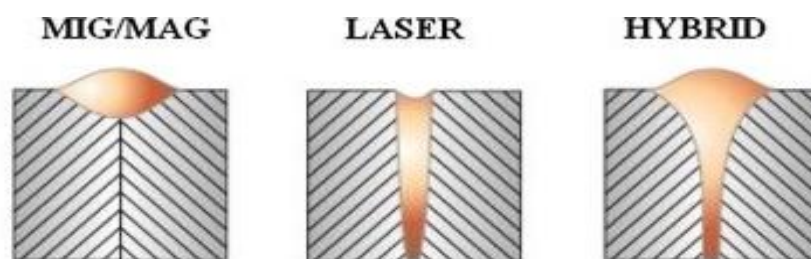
Схемы формирования сварных швов при дуговой сварке, лазерной сварке и гибридной лазерно-дуговой сварке [5].
